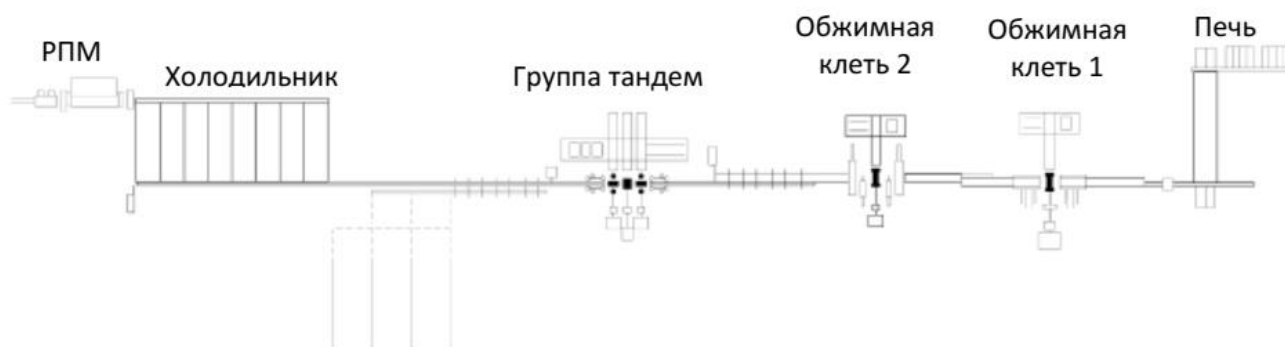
Схема расположения оборудования рельсобалочного стана
